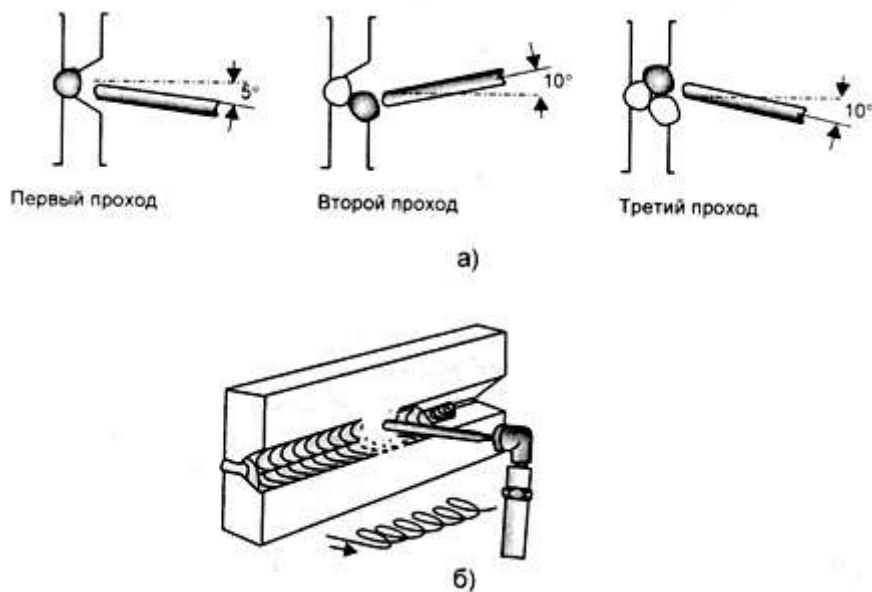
Положение электрода при сварке стыкового соединения в горизонтальном положении: сварка с поперечными колебаниями электрода; пример поперечных движений торца электрода.
